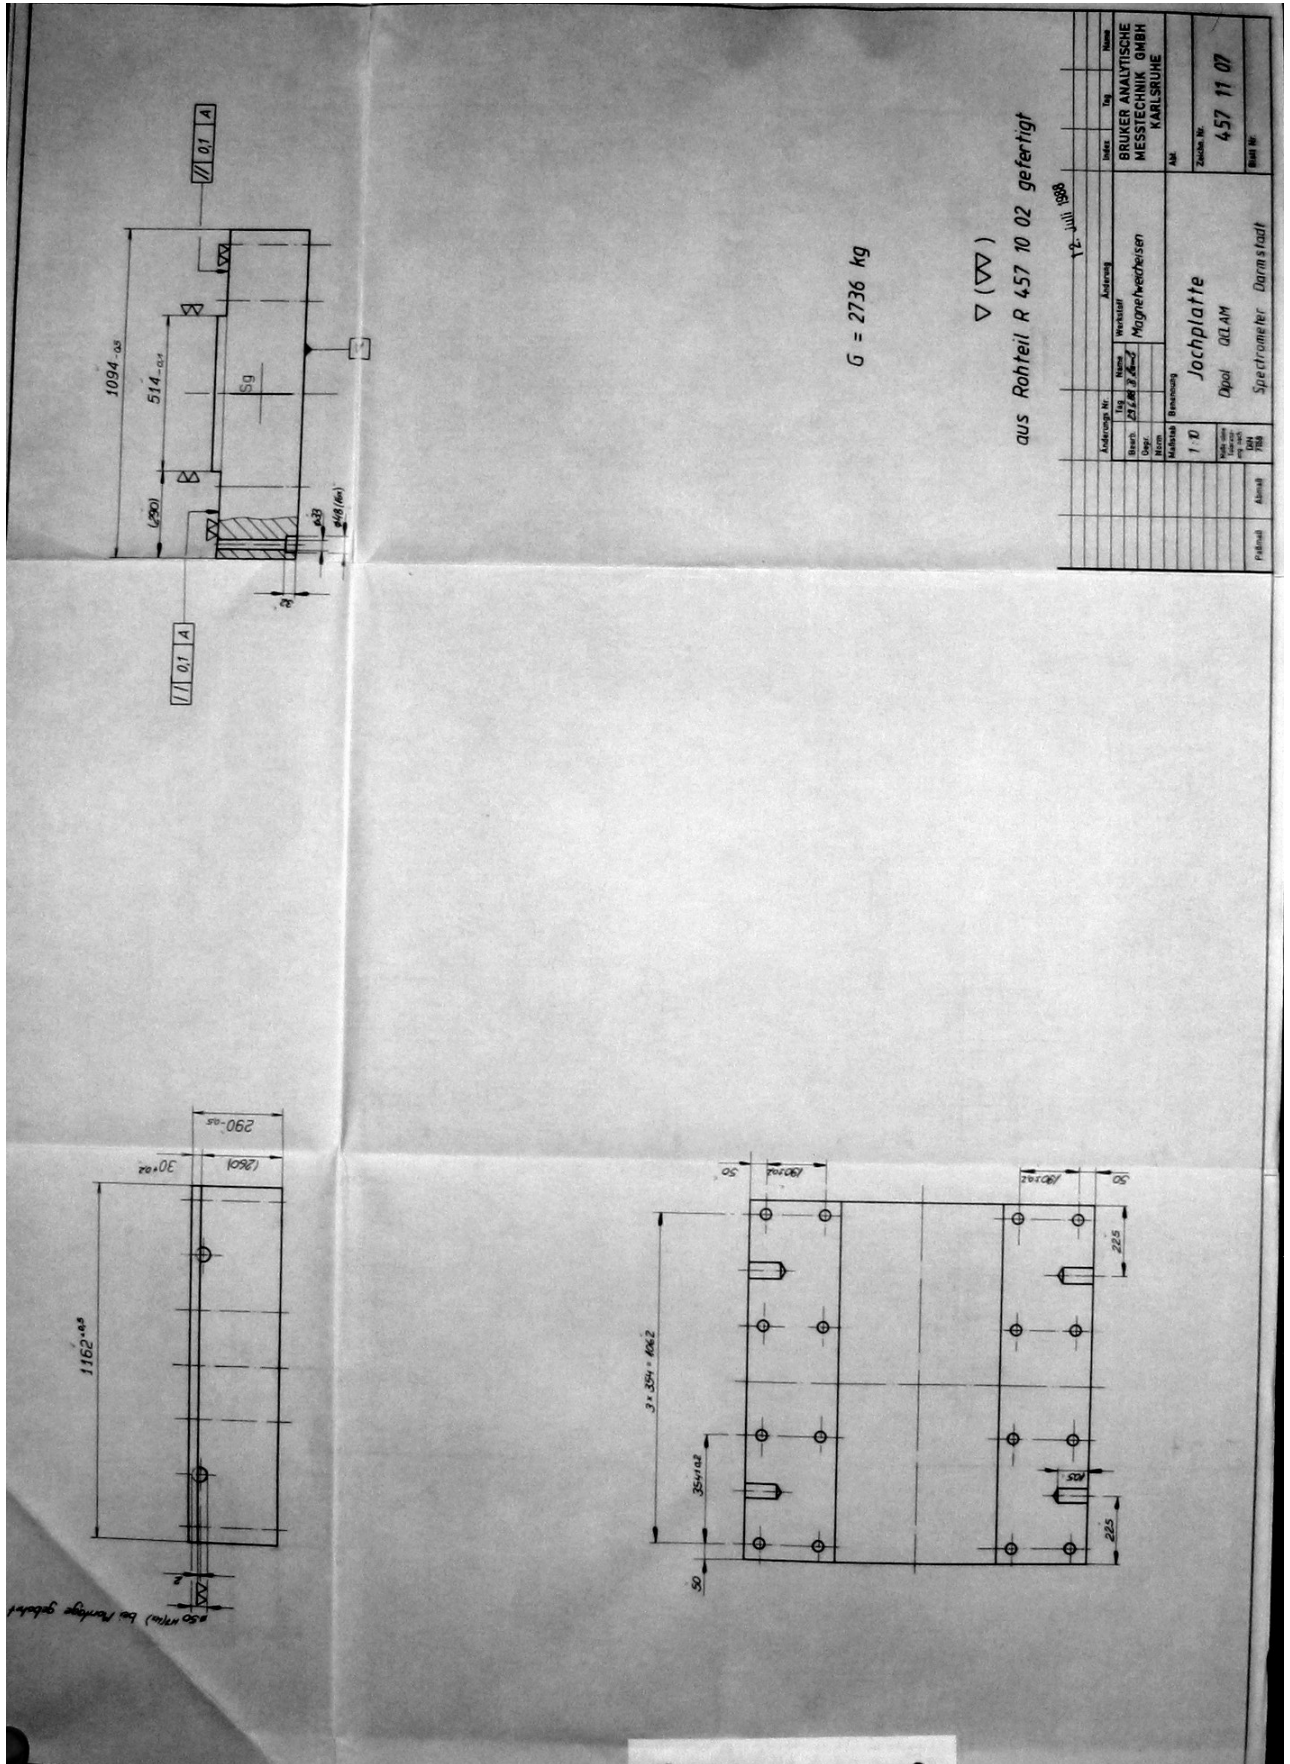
Technische Zeichnung der unteren Jochplatte des QClams.
